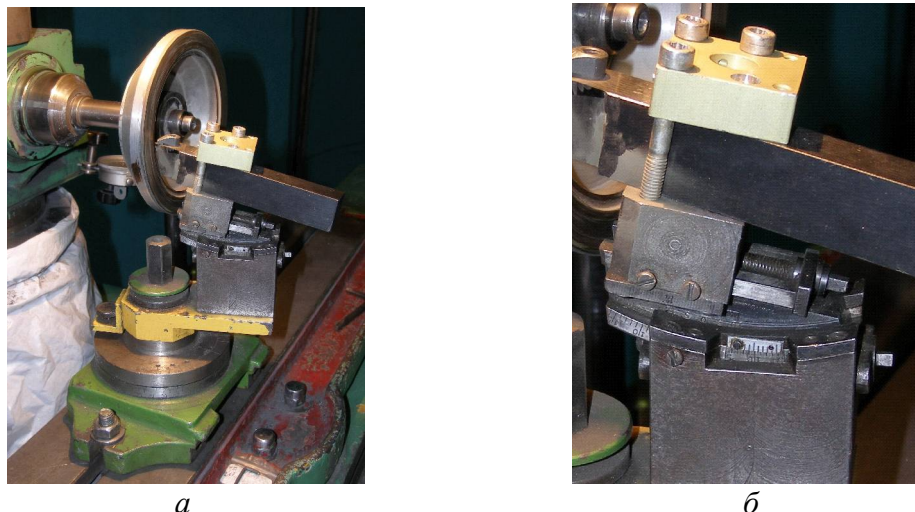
Поворотное приспособление для профилирования и доводки резовых вставок по задней поверхности (а); установка заднего угла (б).
